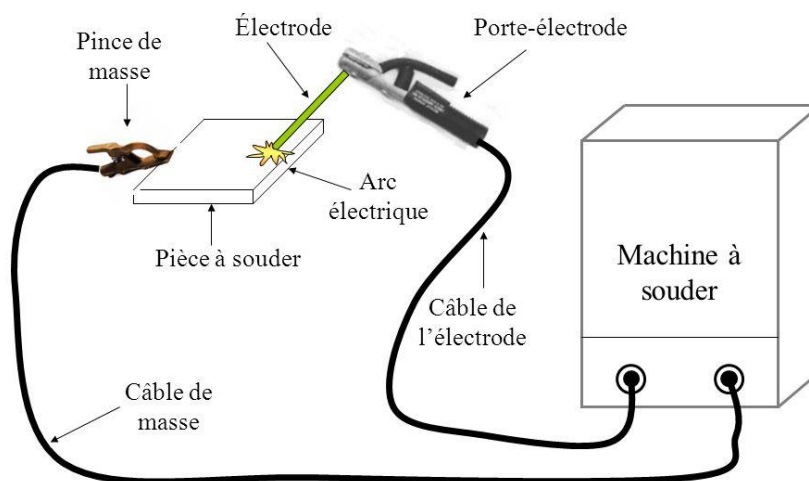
circuit de soudage à l'arc enrobée
